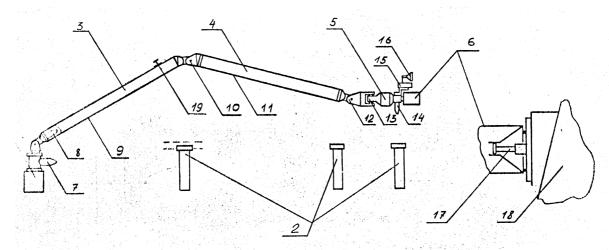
Манипулятор: 1 — корень манипулятора; 2 — ложементы; 3 — плечевое звено; 4 — локтевое звено; 5 — кистевое звено; 6 — захватное устройство; 7 — шарнир рыскания плеча; 8 — шарнир тангажа плеча; 9 — соединительная труба; 10 — шарнир тангажа локтя; 11 — соединительная труба; 12 — шарнир тангажа кисти; 13 — шарнир рыскания кисти; 14 — шарнир ротации кисти; 15 — телекамера; 16 — светильник; 17 — такелажный элемент; 18 — объект манипулирования; 19 — такелажный элемент плечевого звена.
